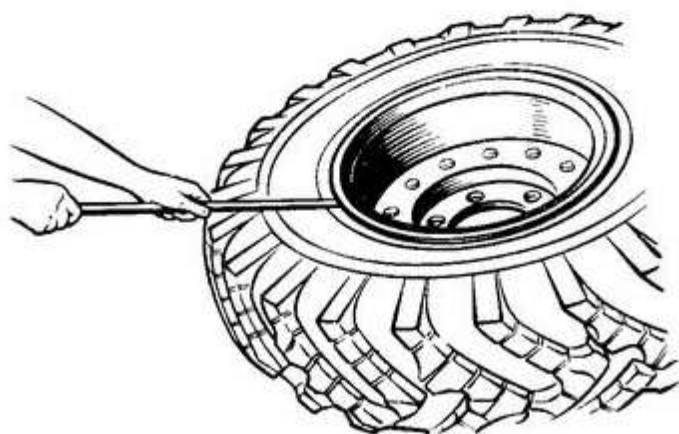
Отжатие бортового кольца шины вилочной лопаткой
